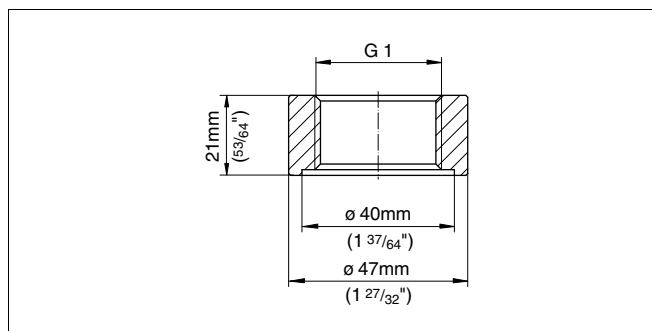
Размеры приварного штуцера G1 A по ISO 228-1
